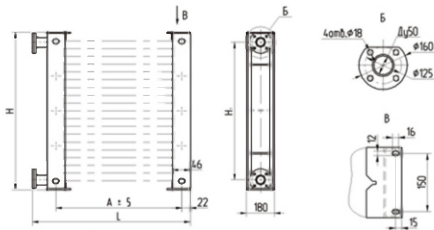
Габаритно-присоединительные размеры ТБЗ- ...
